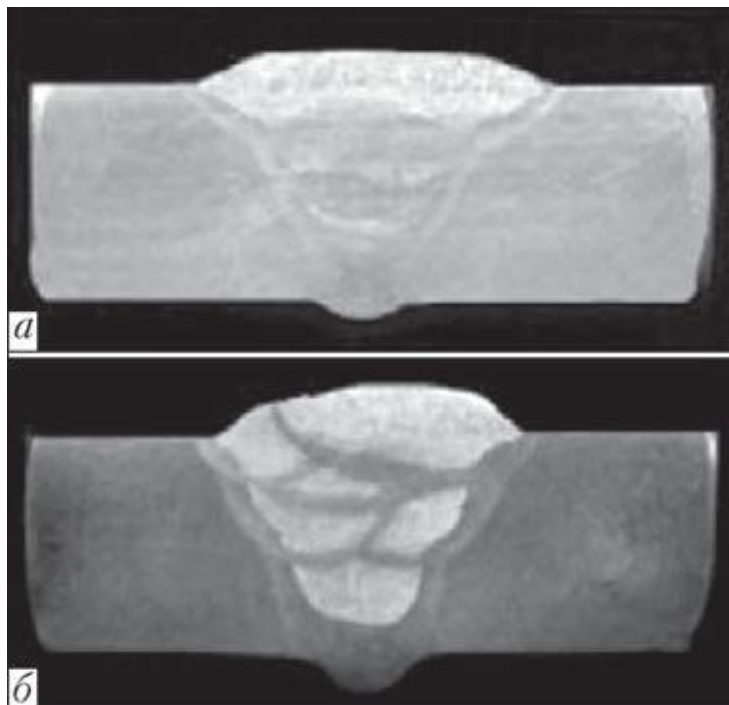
Макрошлиф стыкового сварного соединения: сварка методом «один слой за один проход» (а); сварка ниточными валиками (б)
